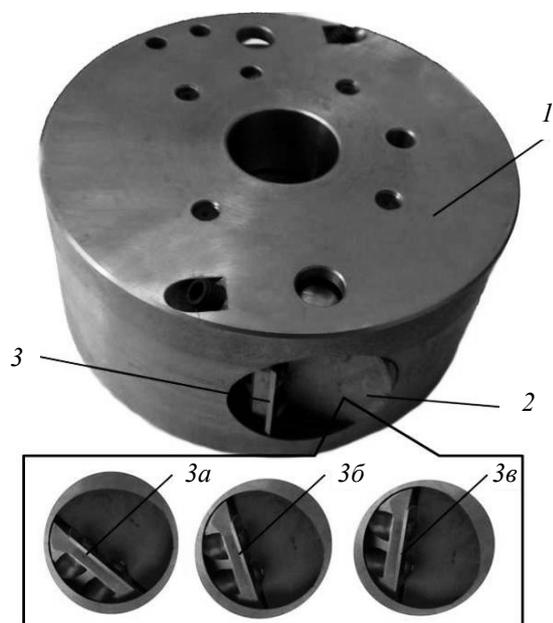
Фреза сборная с изменяемым передним, задним углами и углом наклона кромки: 1 – корпус; 2 – элемент крепления ножа; 3 – нож; 3а, 3б, 3в – варианты положения ножа
